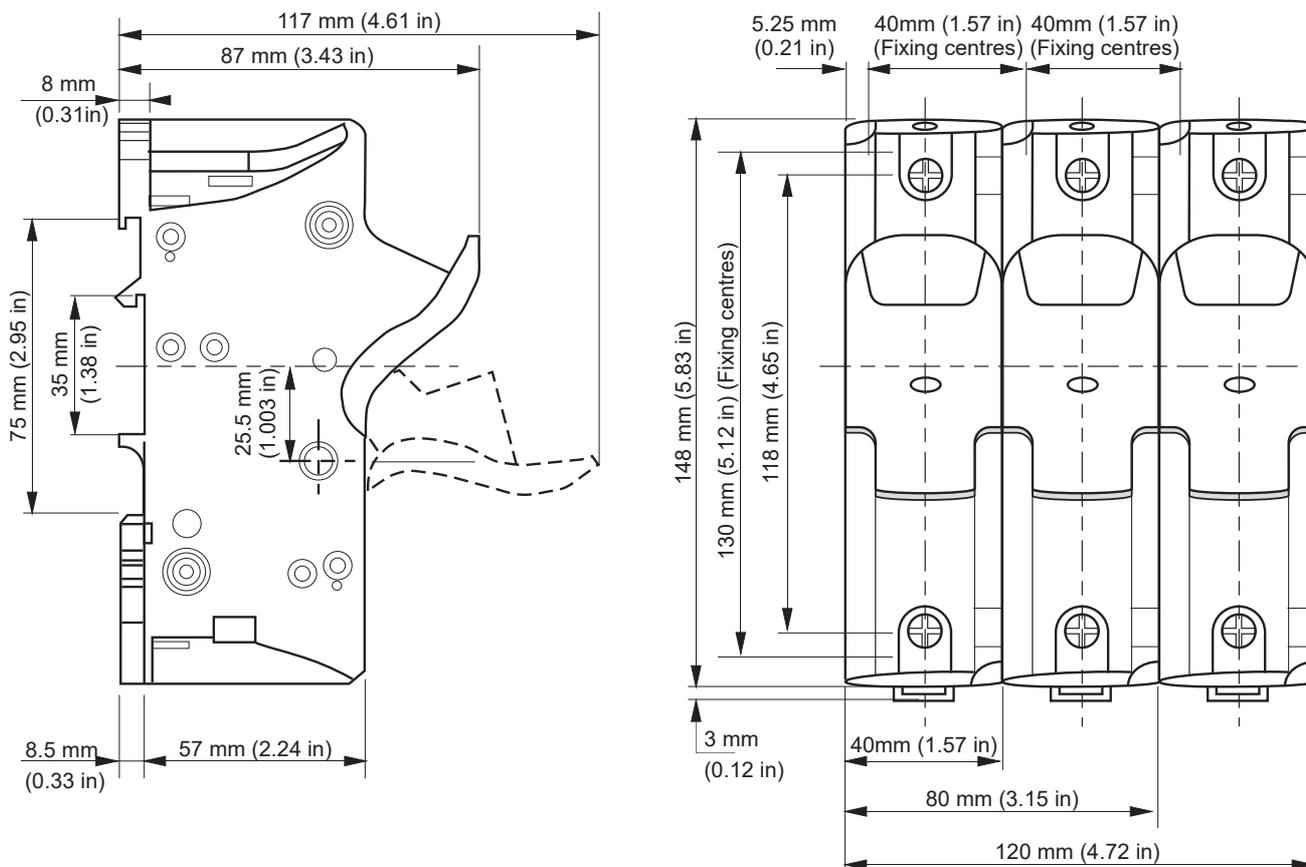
Dimensions des porte-fusibles : US271 (27x60 mm)
